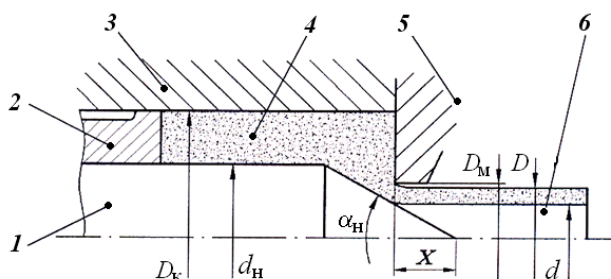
Схема процесса прямого прессования с использованием конической пресс-иглы: 1 – коническая пресс-игла; 2 – пресс-штемпель; 3 – контейнер; 4 – исходная заготовка; 5 – матрица; 6 – отпрессованная труба
